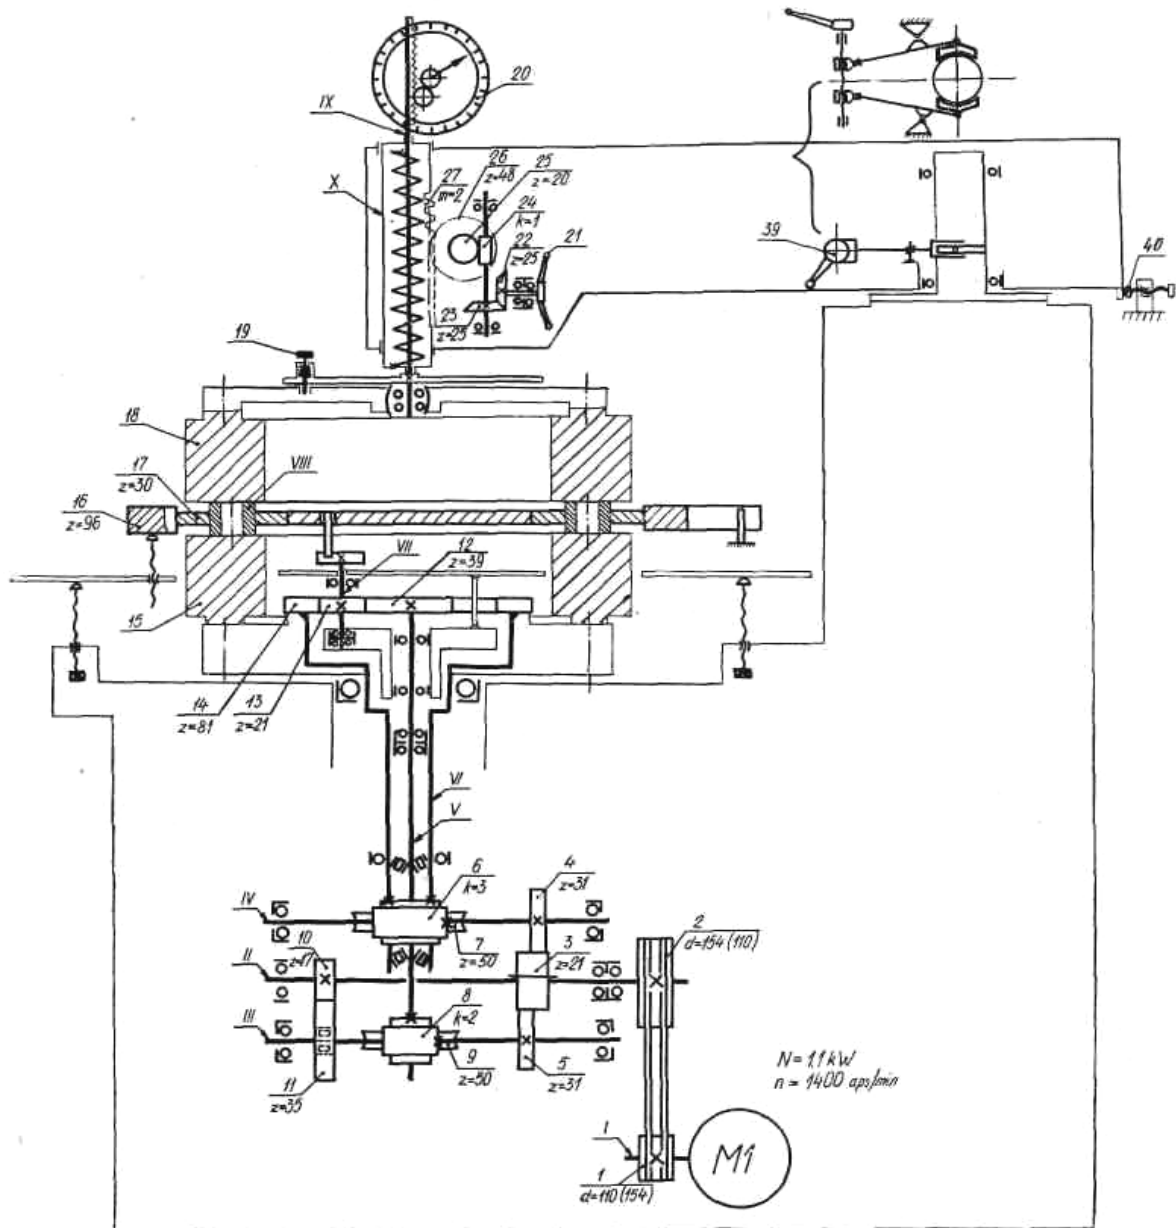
Кинематическая схема универсального притирочного станка модели 3Б814
